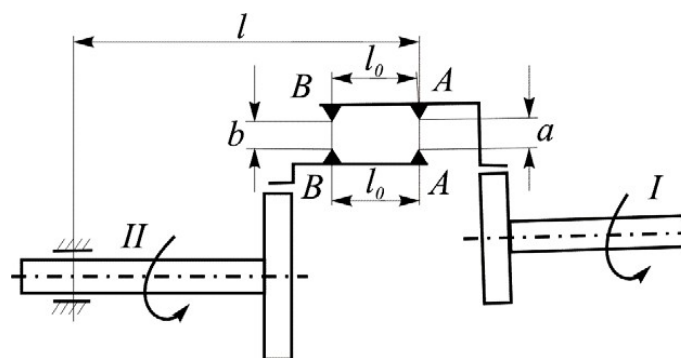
Схема для центровки валов по радиально-осевым стрелкам: I – базовый вал; II – центрируемый вал
